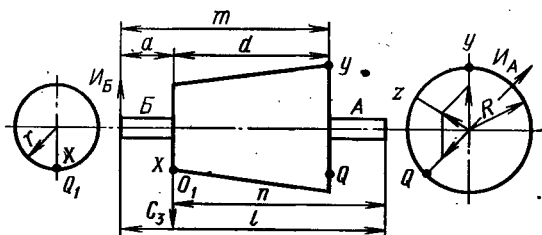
Схема расположения и корректировки уравновешивающих грузов
